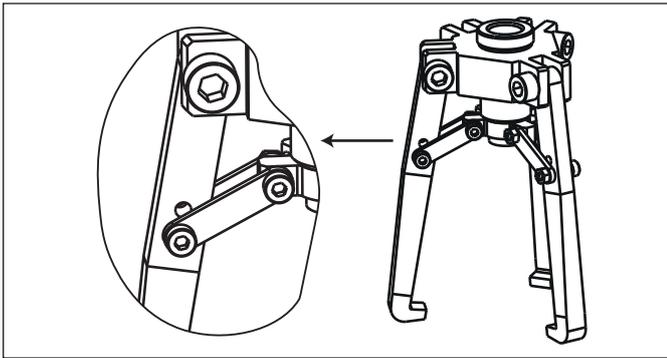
Detalle de instalación para la configuración externa con garras estándar
